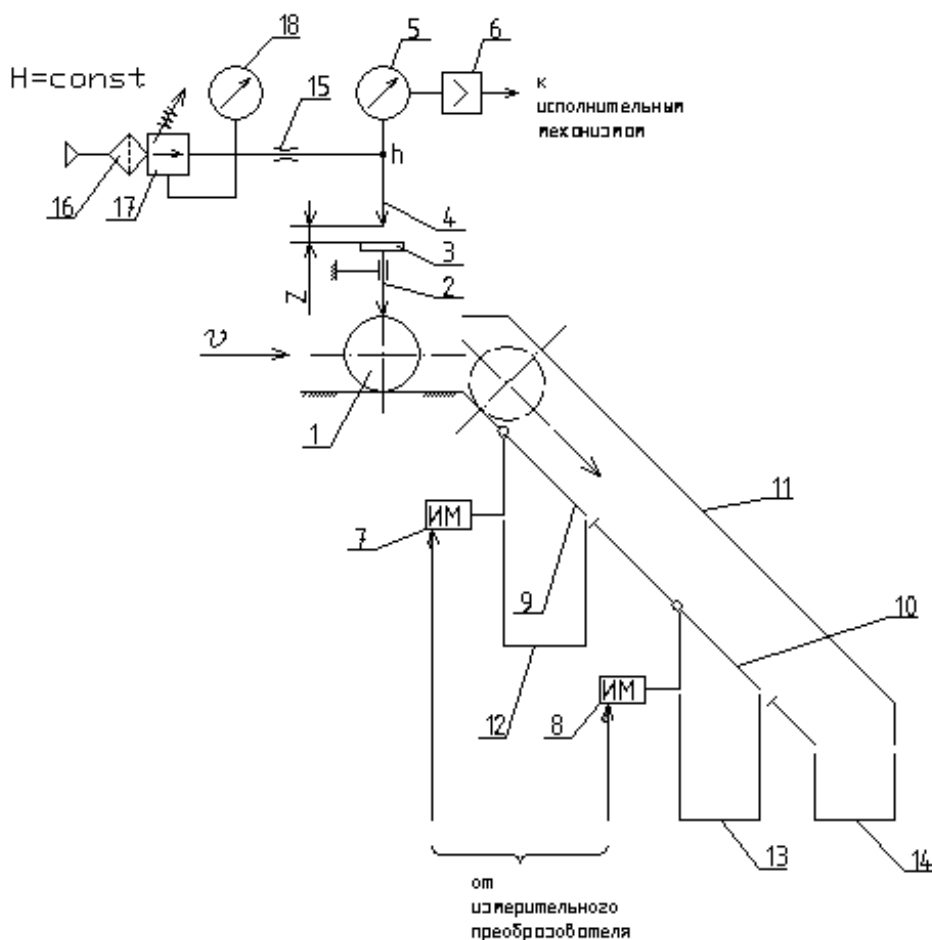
Схема контрольно-сортировочного автомата
